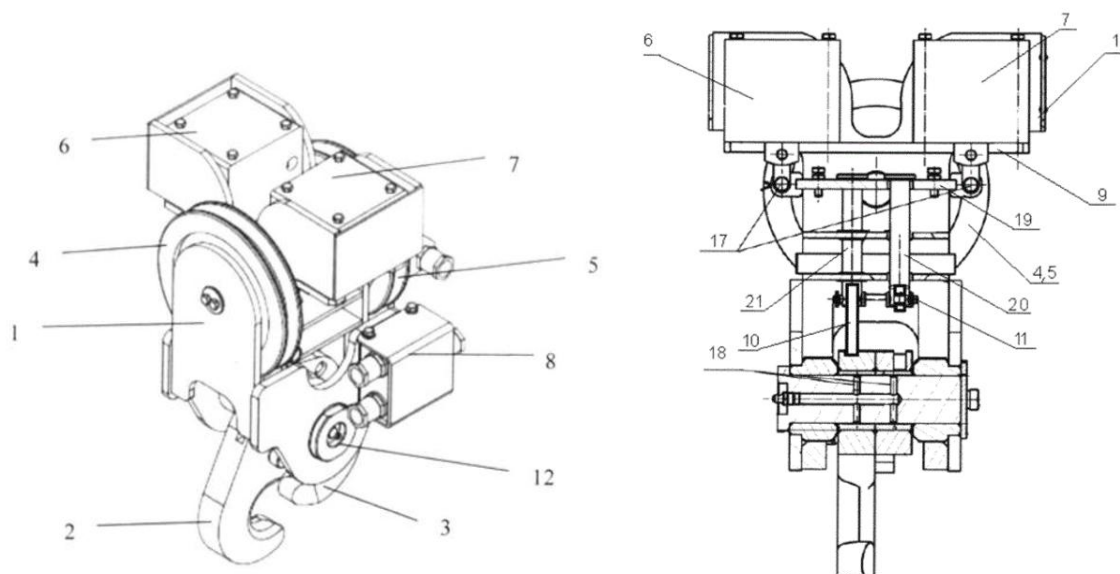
Общий вид и вид сбоку автоматического захватного устройства
